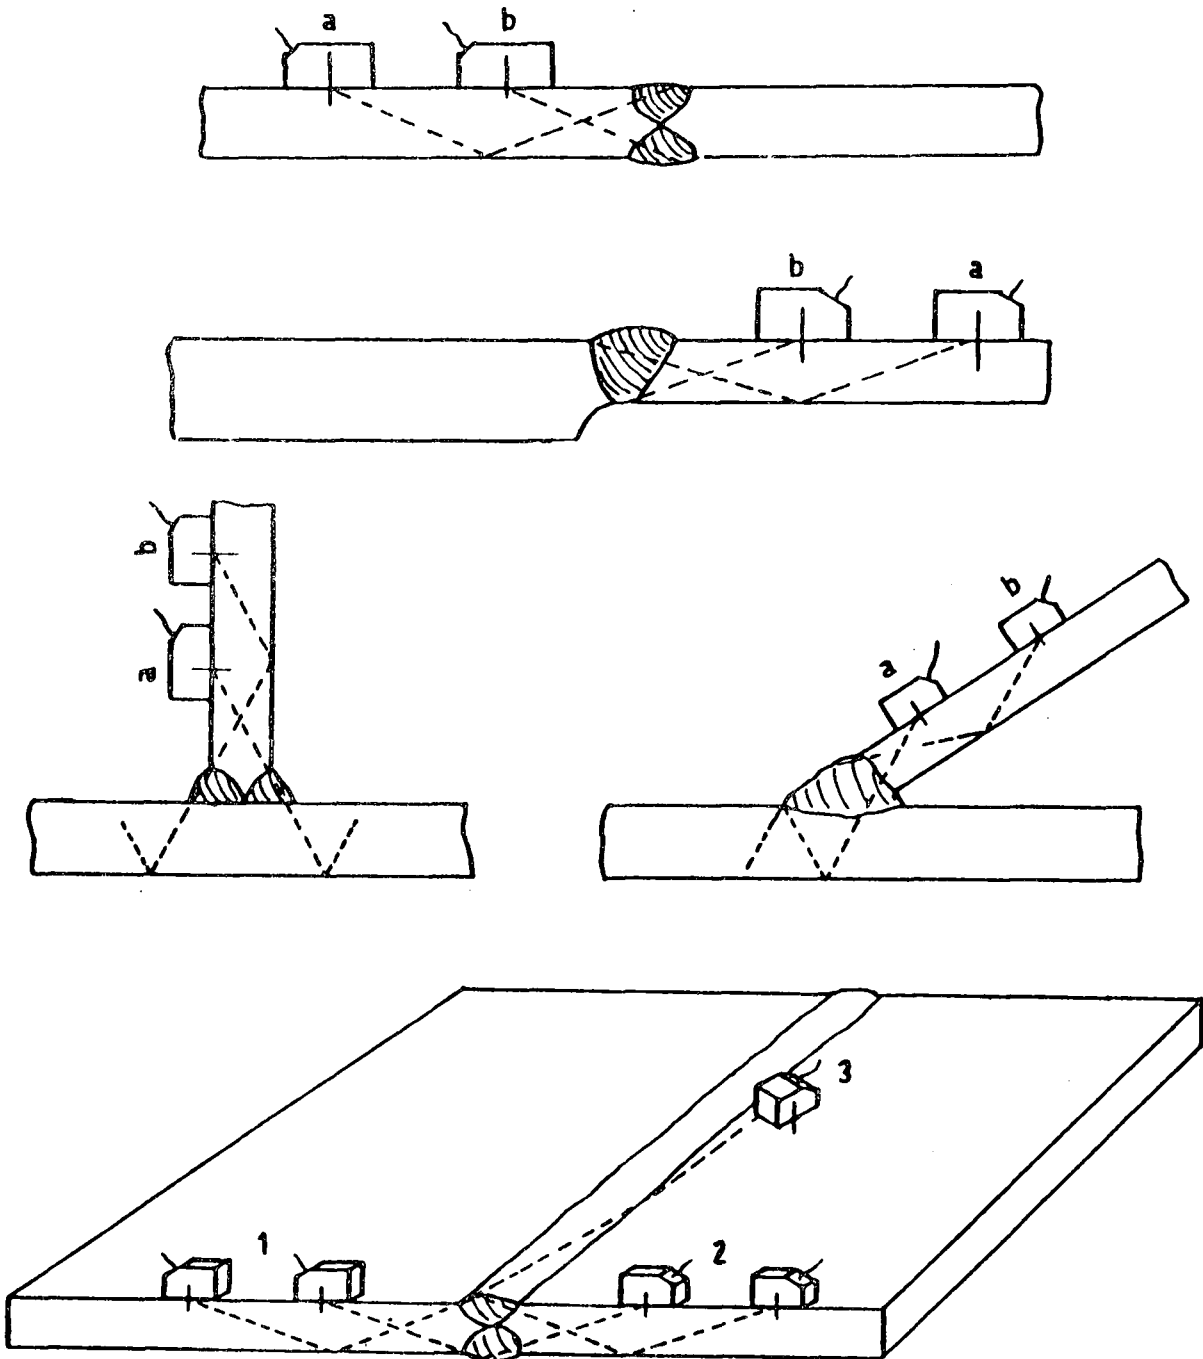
EXAMEN DE SOLDADURAS POR ULTRASONIDOS.
